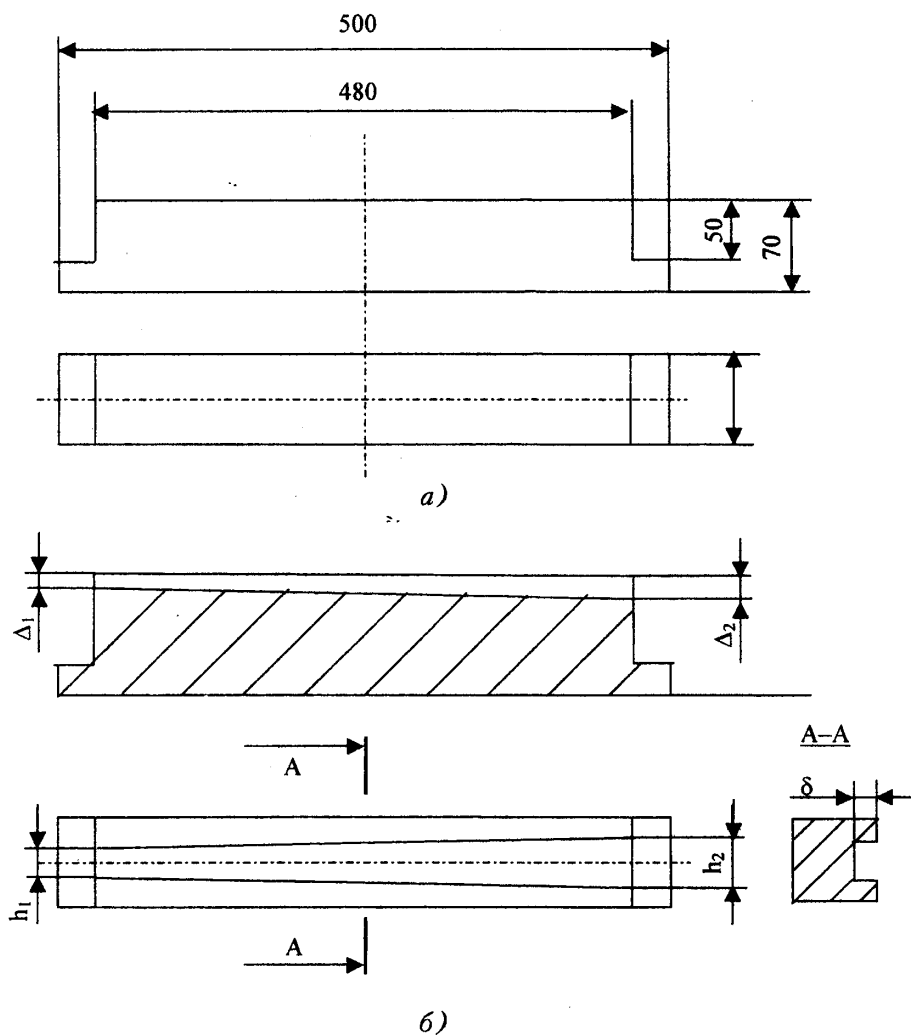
Заготовки, які використовувались при дослідженнях процесу обробки фрезами косокутного різання: а – заготовка із суцільною поверхнею; б – заготовка з пазом
